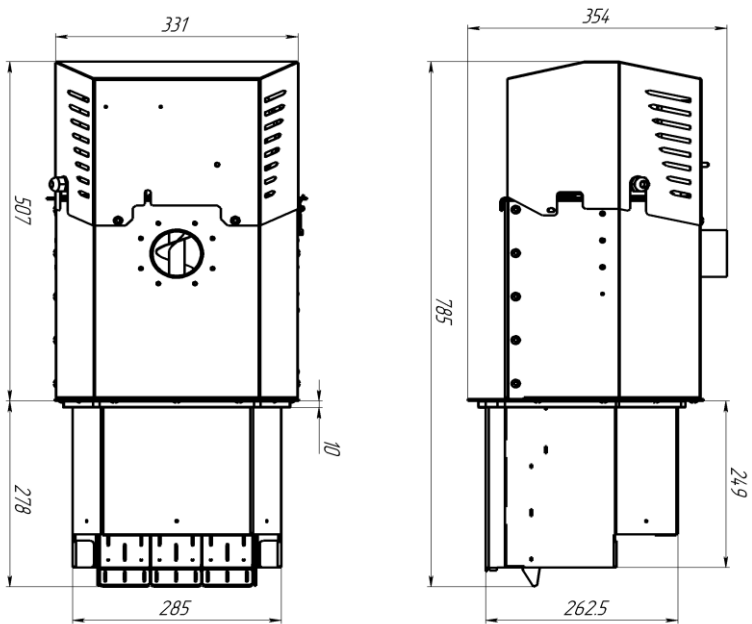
Габаритные и присоединительные размеры пеллетной горелки КУПГ Орима 125 кВт.
